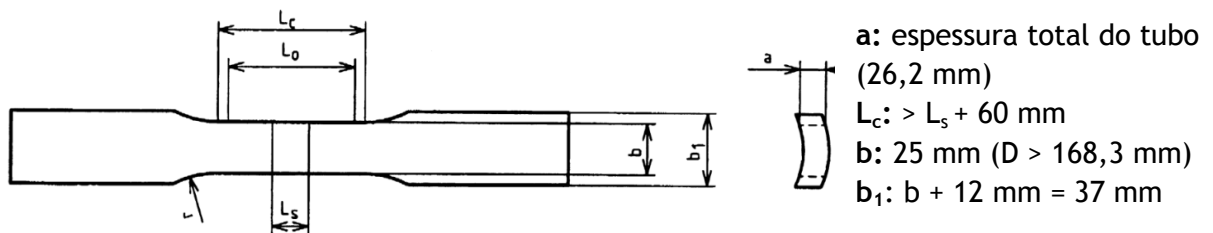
provete de tração transversal à soldadura [47]
